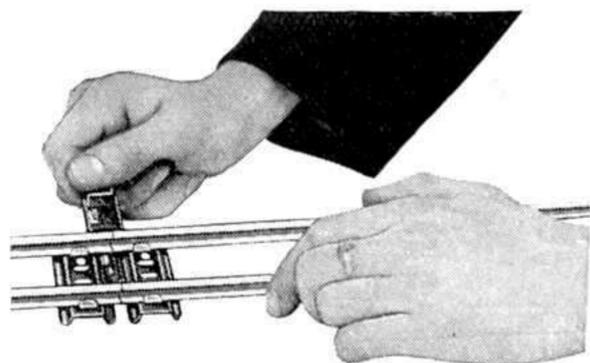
Assemblage de deux rails Hornby à l'aide d'une broche d'assemblage.
